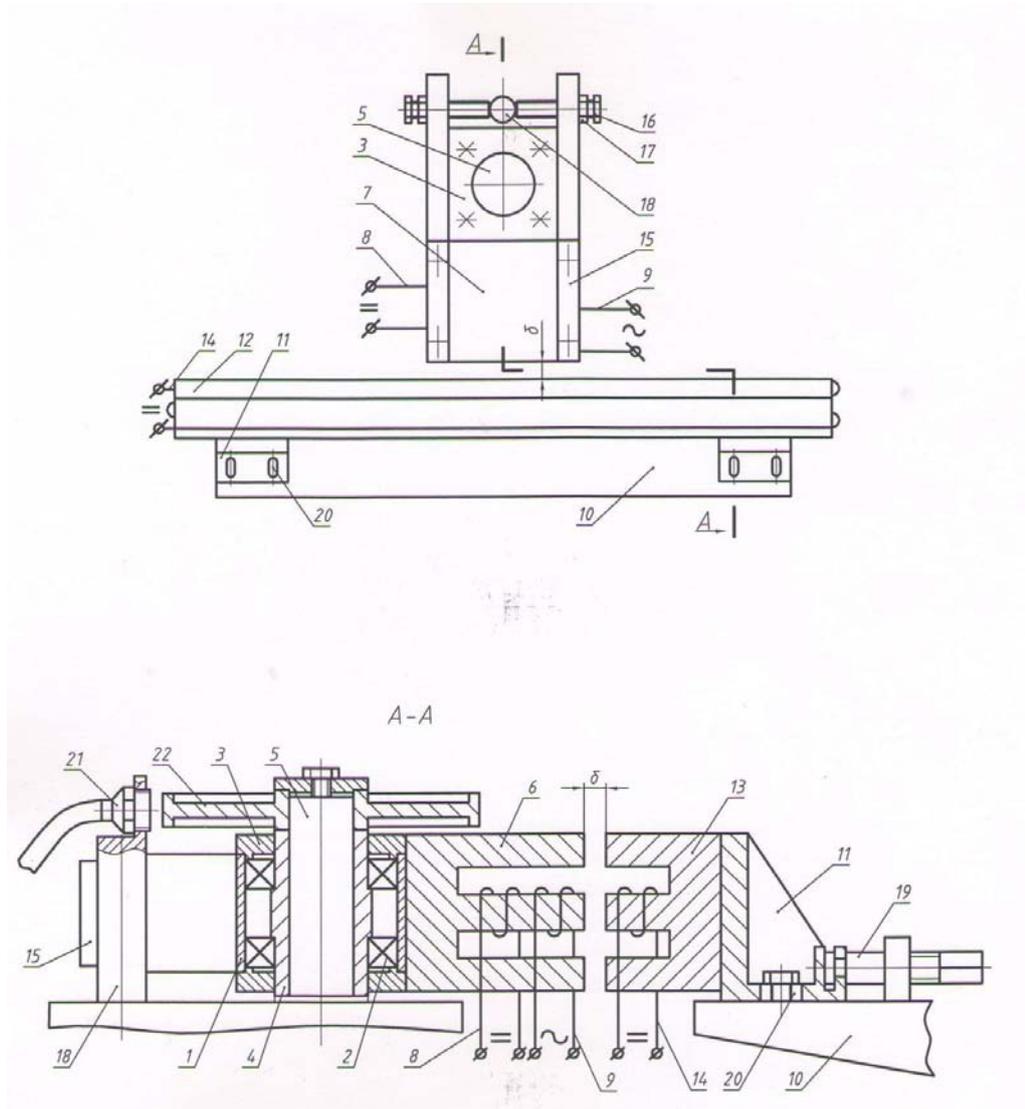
Нагрузочное устройство для испытания фрезерных станков
